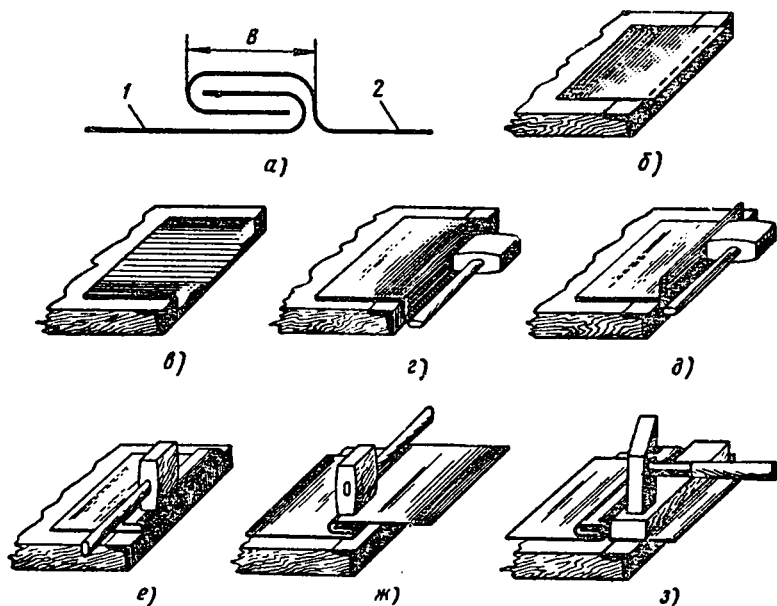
Изготовление одинарного лежащего фальца ручным способом:
